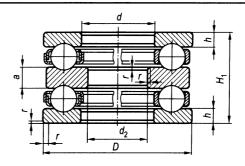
Подшипник шариковый упорный двойной размерной серии 38000H
